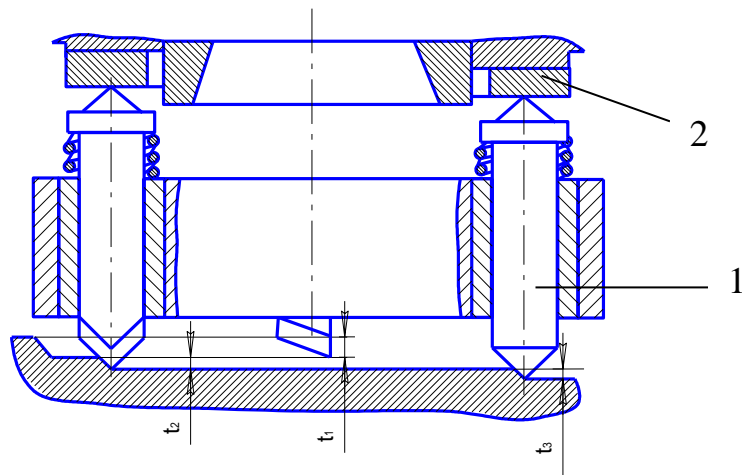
Конструкція торцевої фрези по а. с. 971591, МКИ В 23 С 5/06
